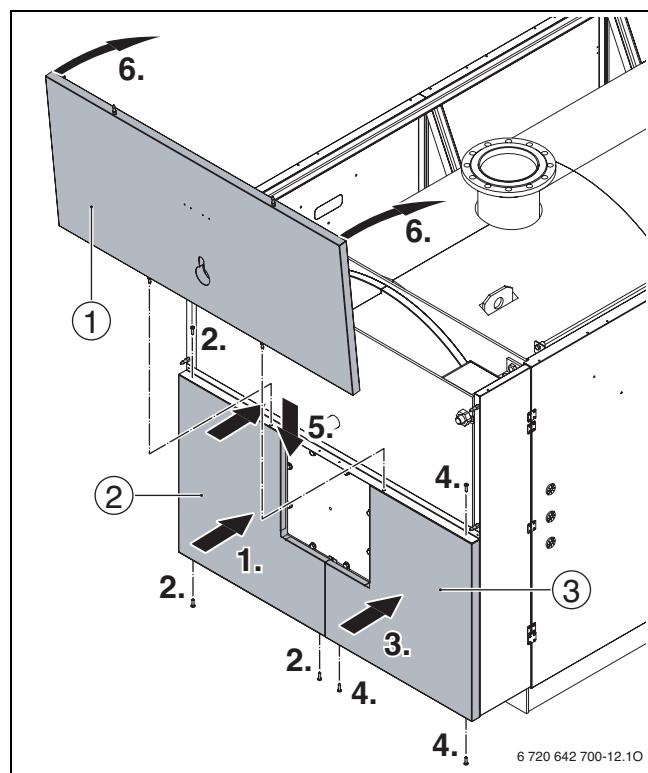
Установка обшивки двери у котлов 1400 - 1850 кВт, третий этап
